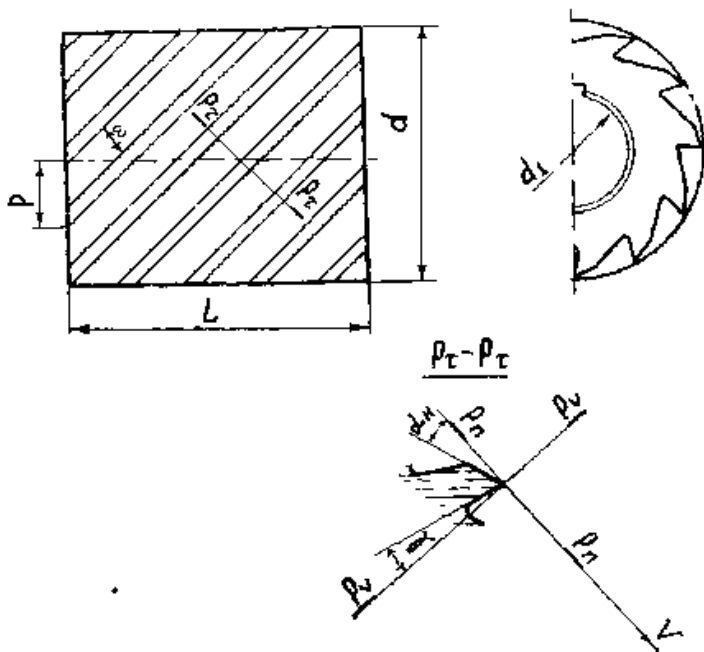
Элементы и геометрия цилиндрической насадной фрезы
